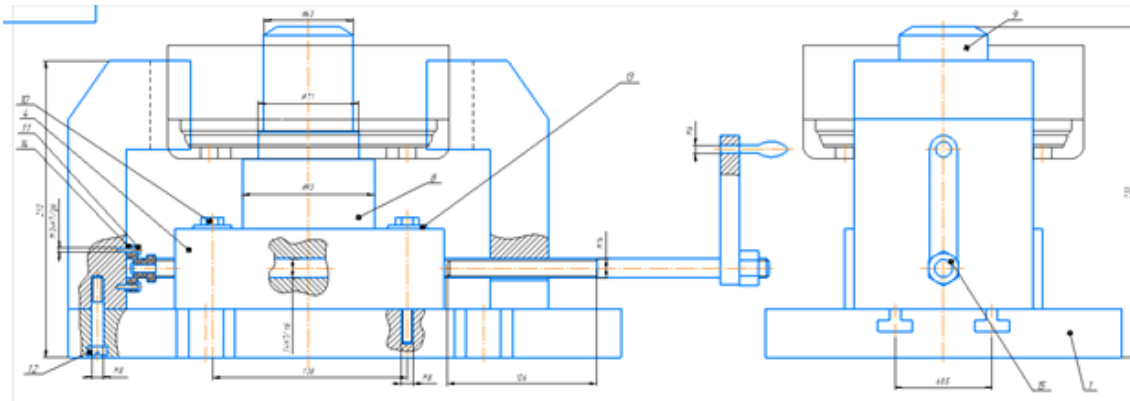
Эскиз приспособления для фрезерования впадин
